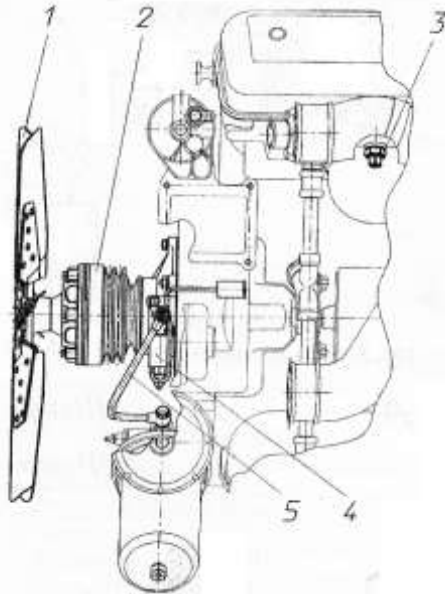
Розташування деталей приводу вентилятора з електромагнітним клапаном на двигуні:
